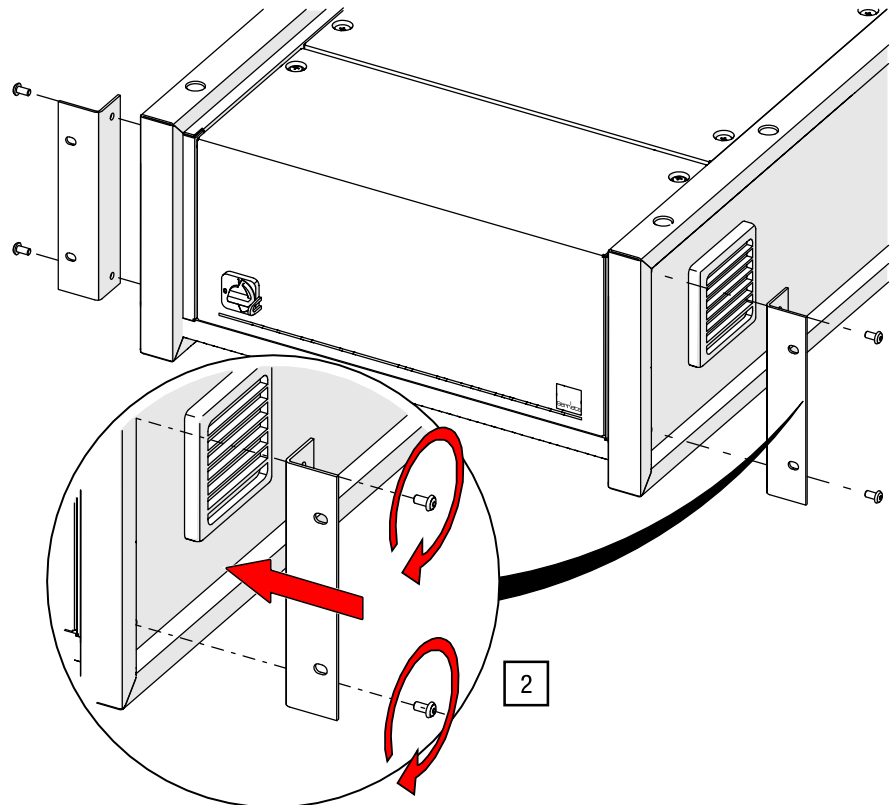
Rack-Montagewinkel anschrauben (Steuerungsmodell kann abweichen)
